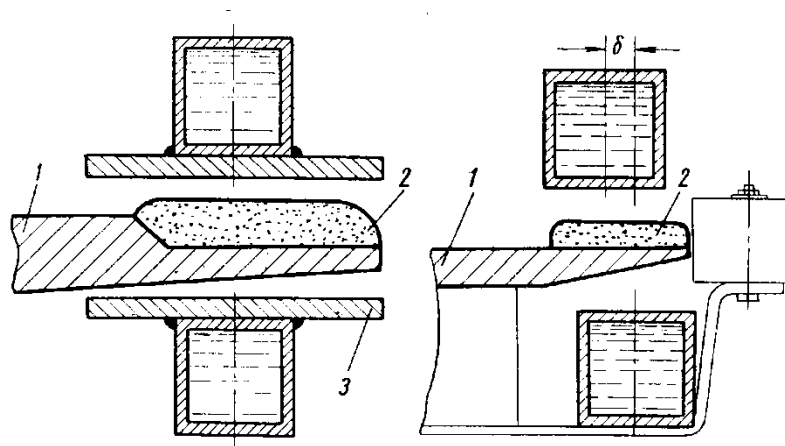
Схема індукційного наплавлення [6]: 1 – деталь; 2 – прошарок шихти; 3 – індуктор
